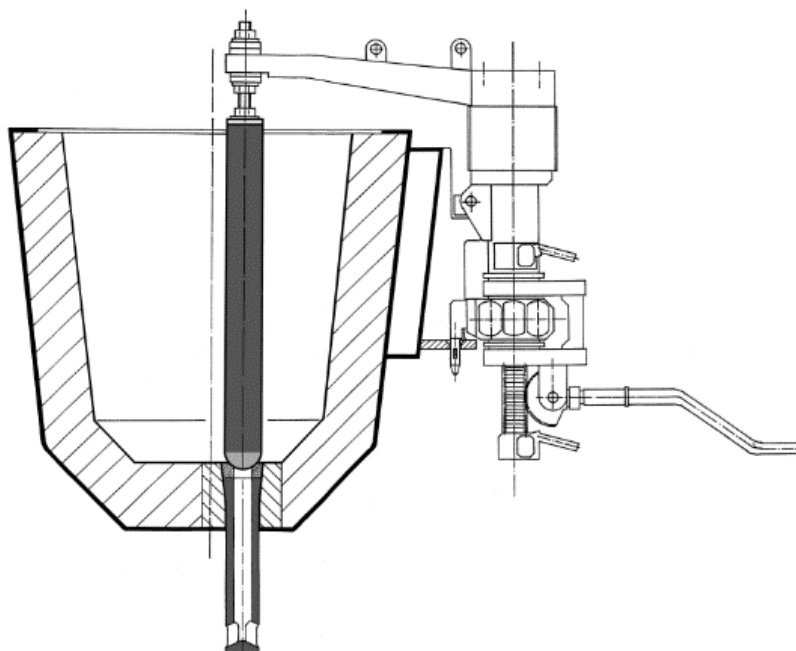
Схема стопорного разливочного устройства промежуточного ковша МНЛЗ
